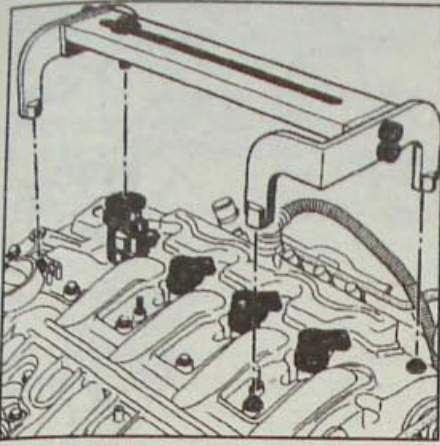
Установка рамки приспособления Mot. 1549 на болты крепления крышки головки цилиндров
